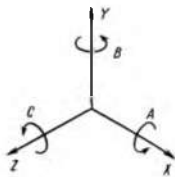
Обозначение движений инструмента и расположение осей координат в станках с ЧПУ
